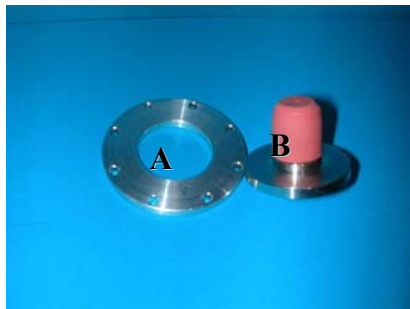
Photo du presse-étoupe et de sa bride de fixation
